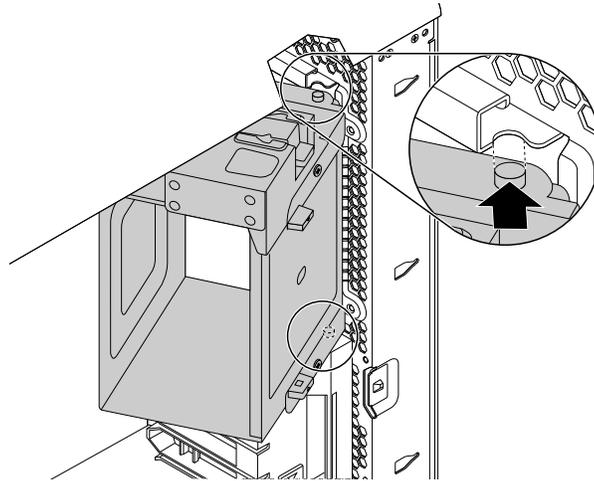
Positionieren Sie die Halterung des optischen Laufwerks im Gehäuse
